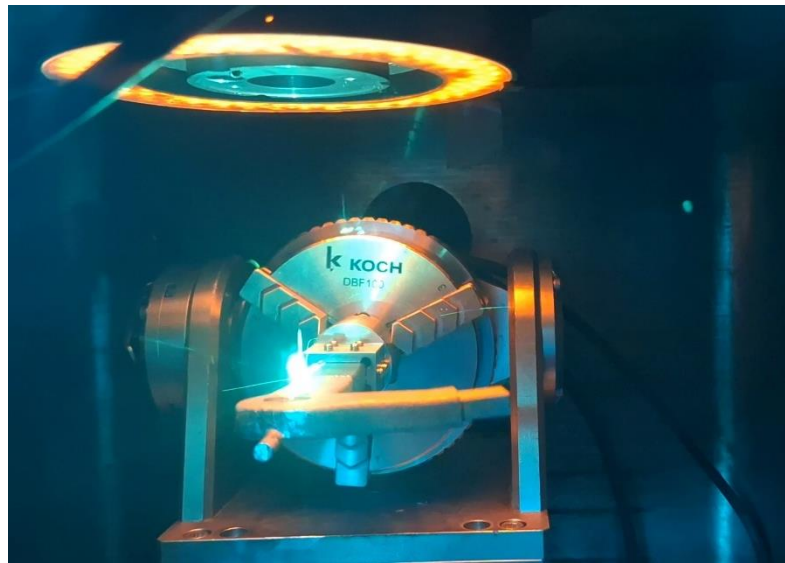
Durchführung der Schweißung an dem Demonstratorbauteil
